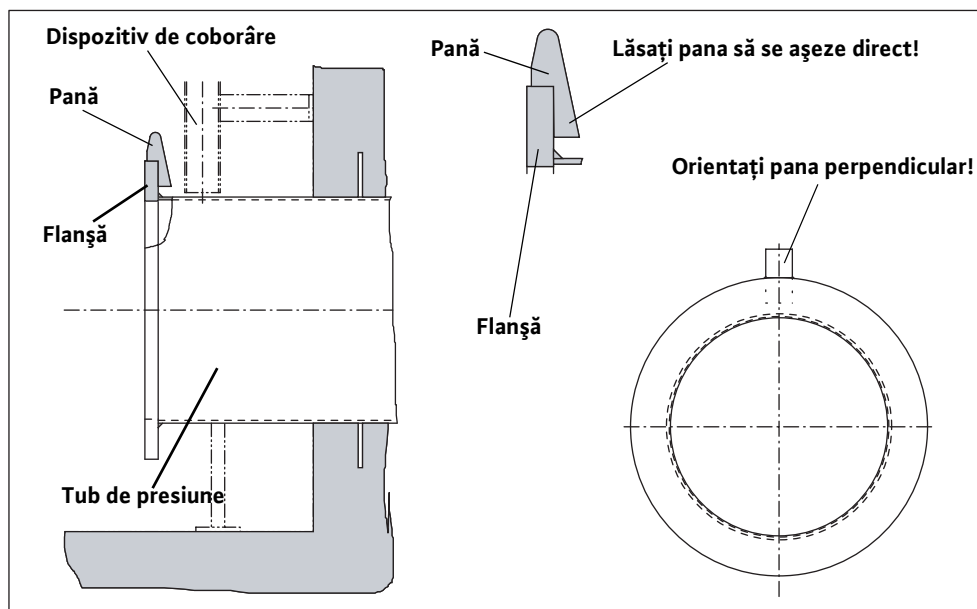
Montare pe tubul de presiune cu inel din oțel
